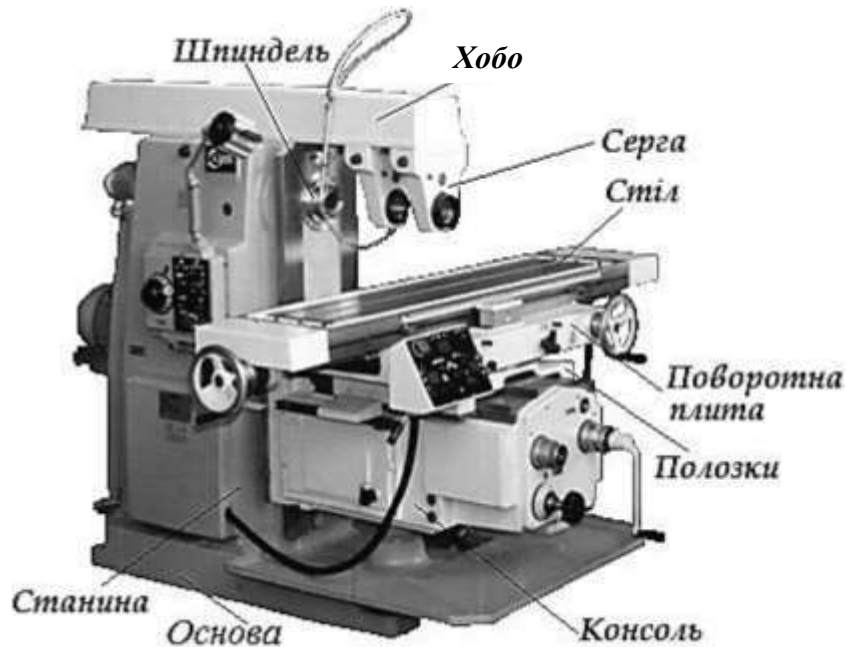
Загальний вид універсально-фрезерного верстата 6М82
